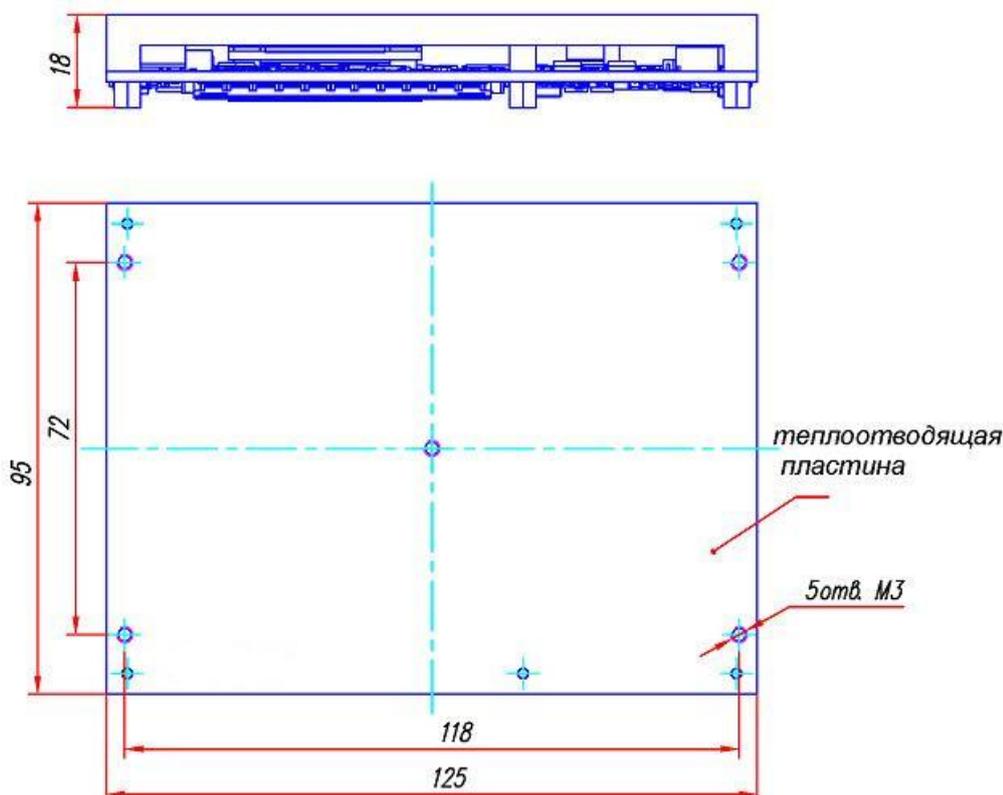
1 - Габаритные и присоединительные размеры изделия
